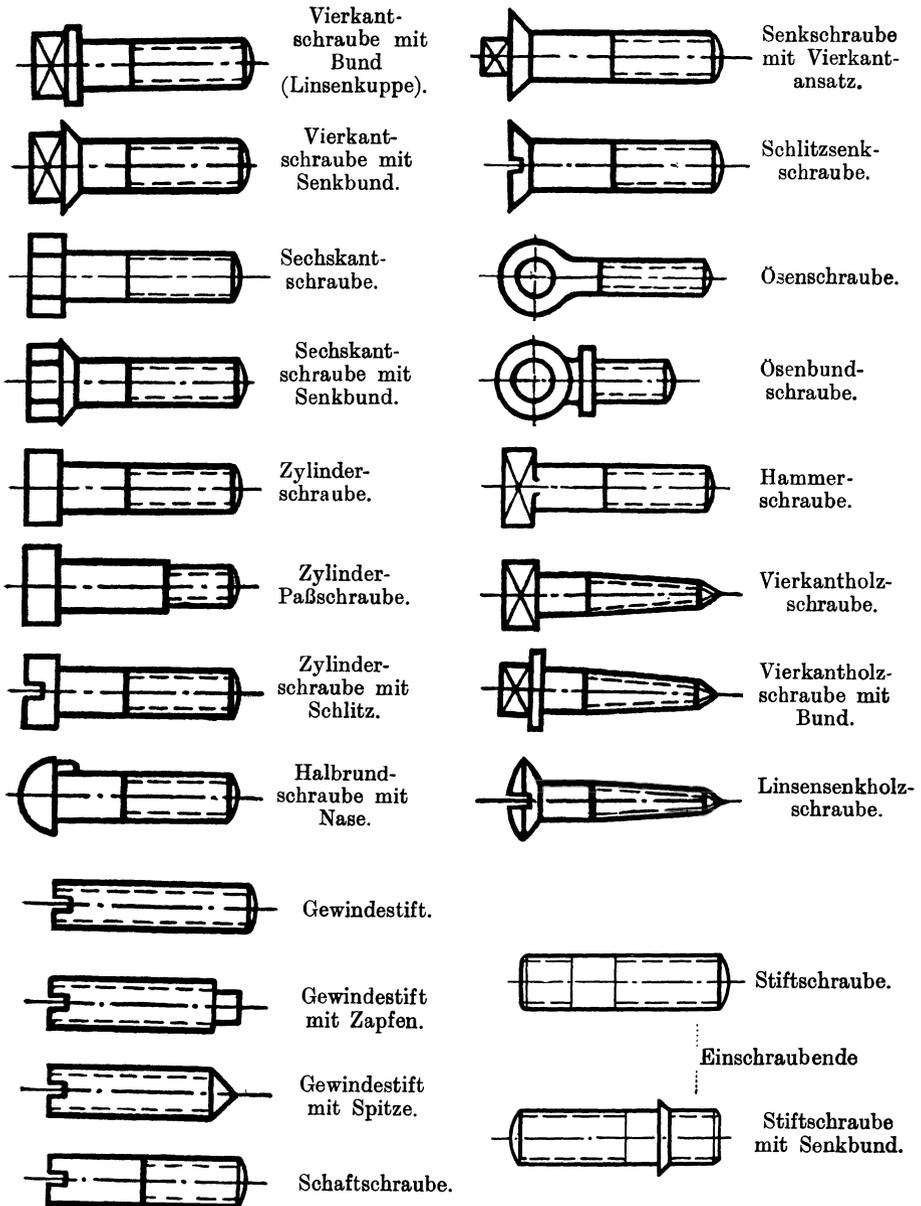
Schraubenarten. (Die Grenzlinie zwischen Schaft und Gewinde (Gewindeauslauf) ist schwach zu ziehen. Vgl. die beiden Stiftschrauben und Abb. 81.)
